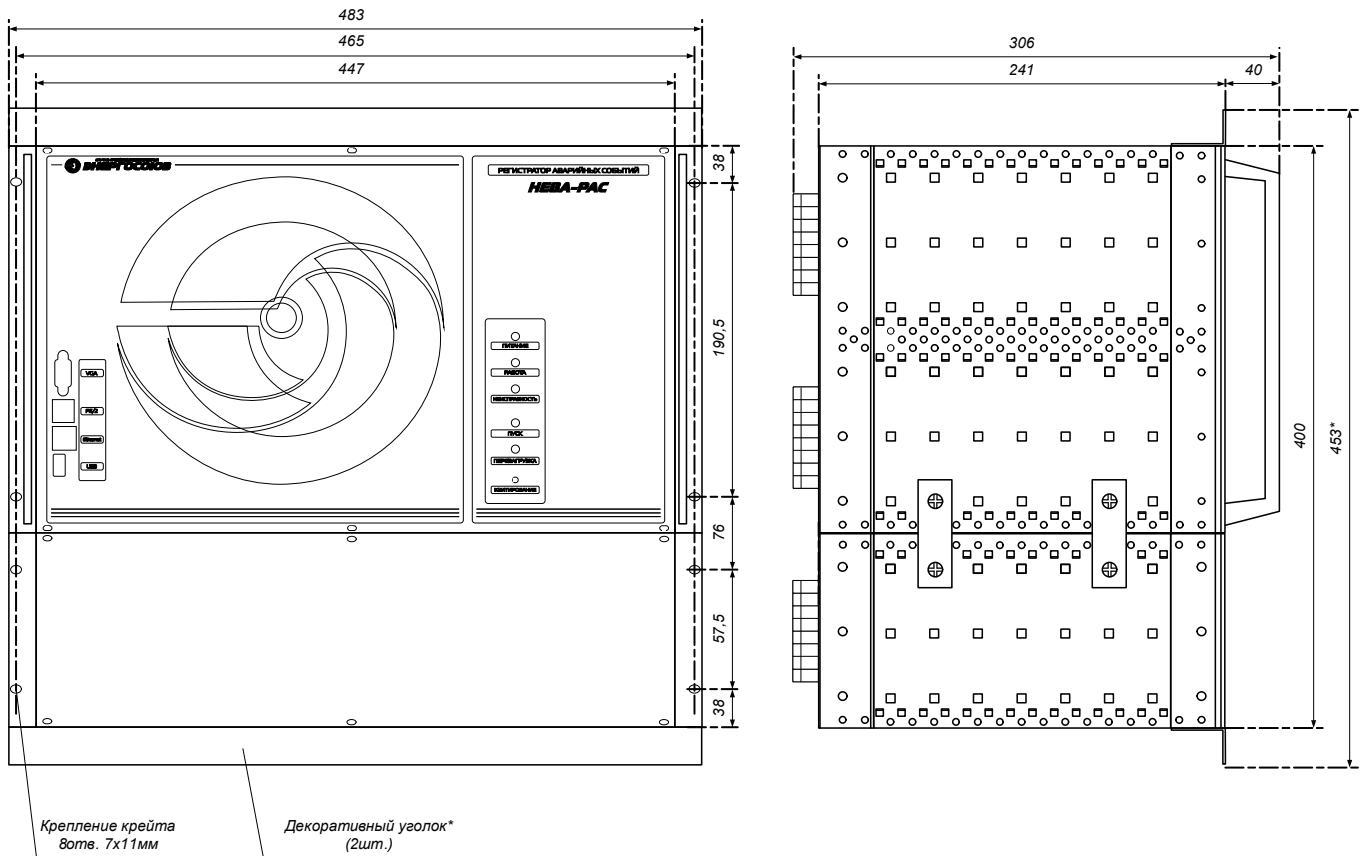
Габаритный чертёж РАС19-4U с установочными размерами
